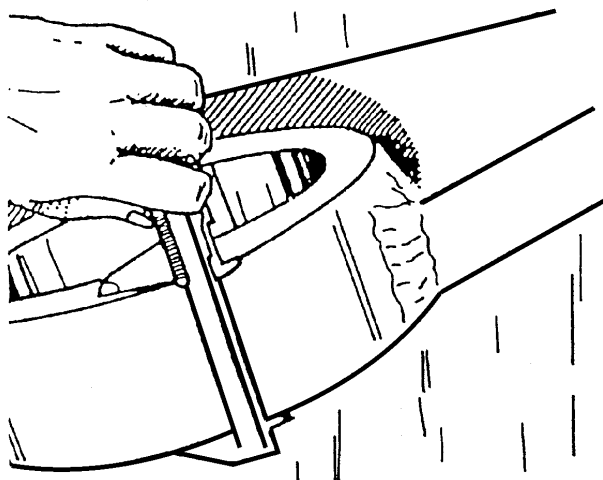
Замер ширины «С» корпуса конических подшипников
